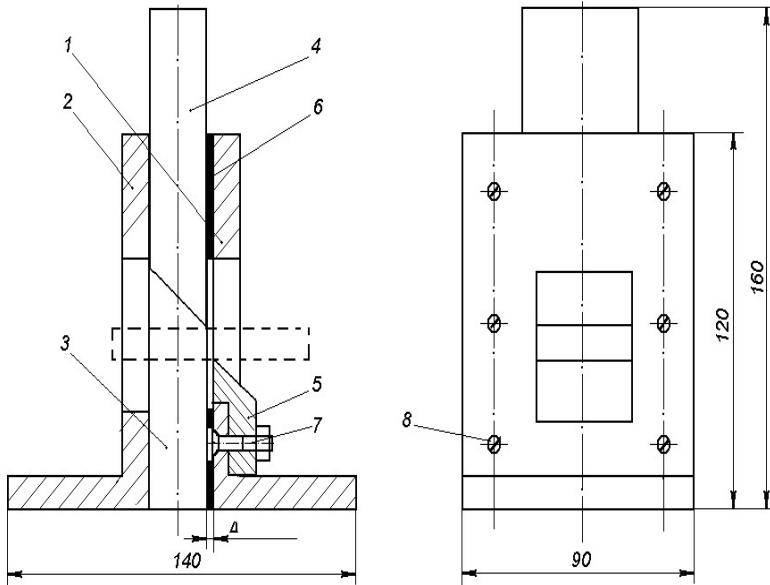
Ескіз пристрою для випробування полімерних матеріалів на зріз двома ножами: 1, 2 – стойки; 3 – вставки; 4 – рухомий ніж; 5 – нерухомий ніж; 6 – прокладка латунна; 7, 8 – гвинти
